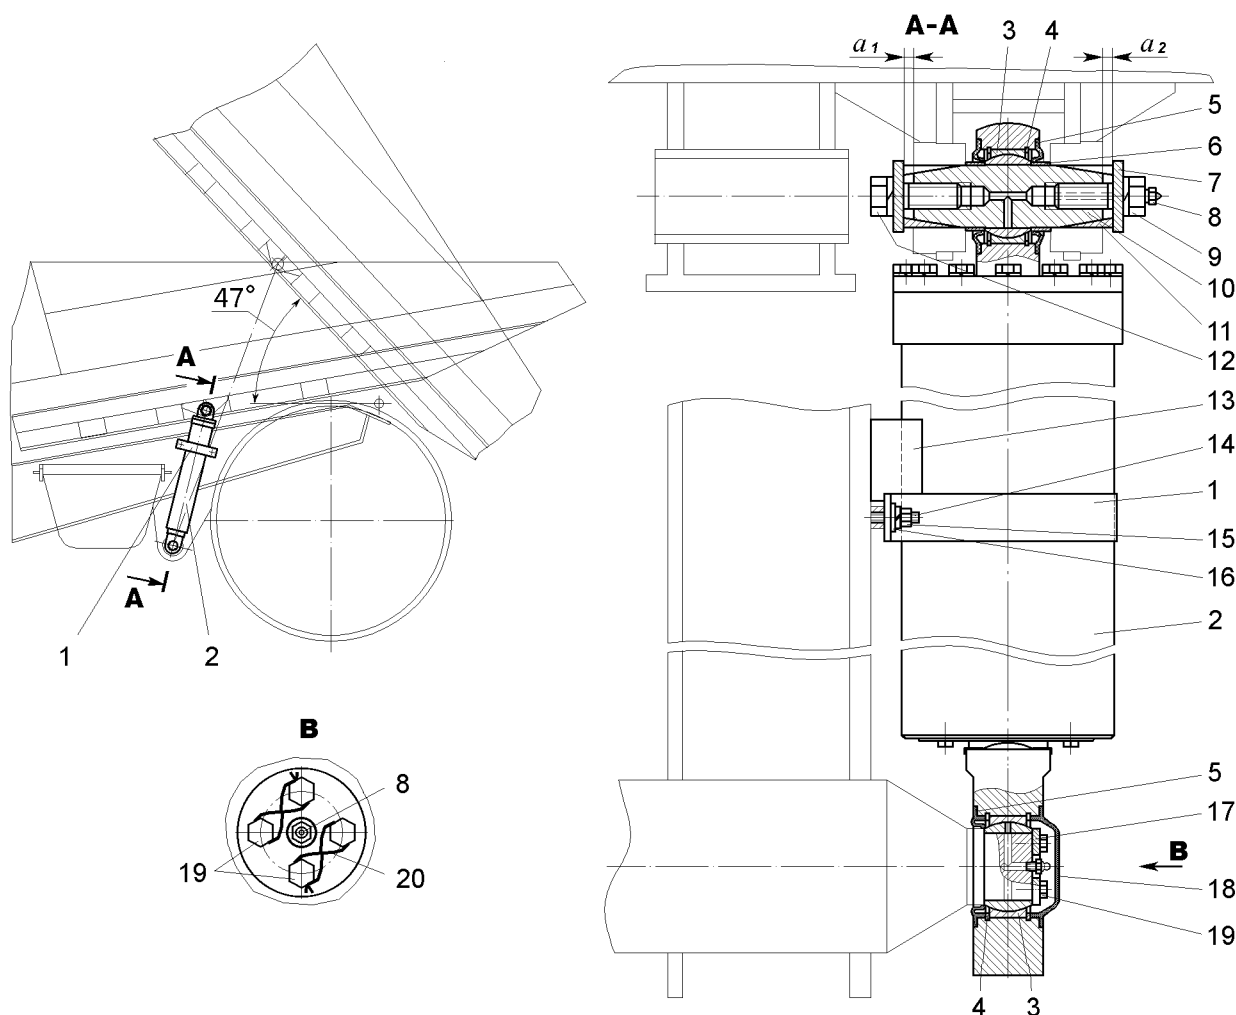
Установка цилиндров опрокидывающего механизма:
